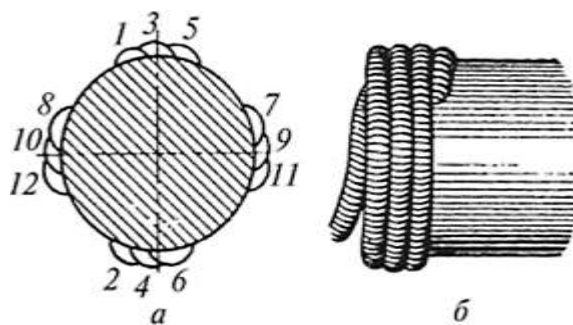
Наплавка шейки вала: а — вдоль оси шейки; б — по окружности
